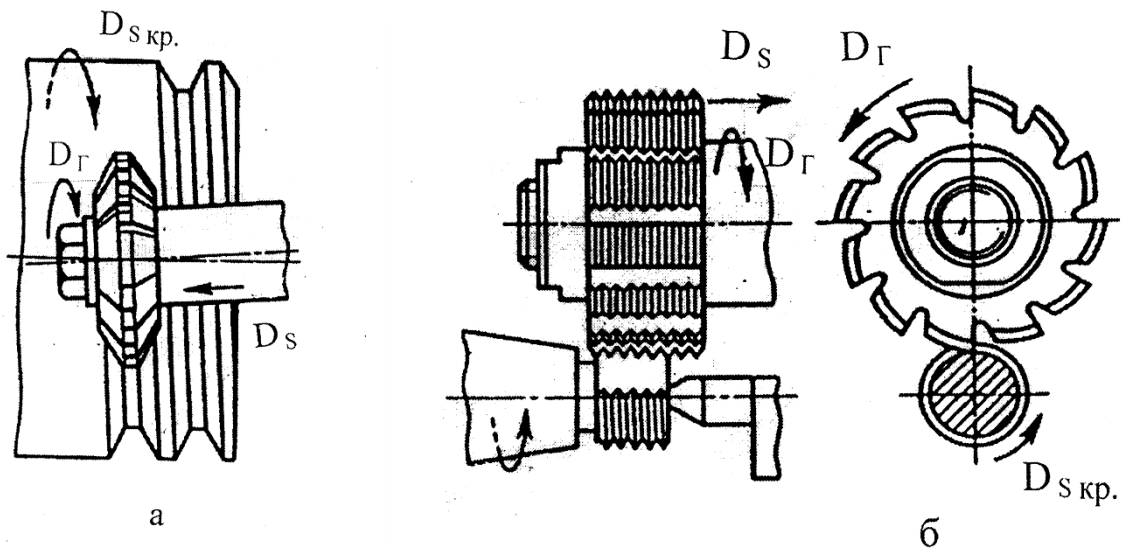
Схема резьбофрезерования наружной поверхности:
